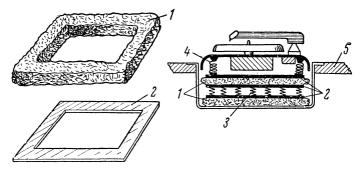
Способ эластичной подвески платы проигрывателя в установке и детали демпфирующего устройства.
